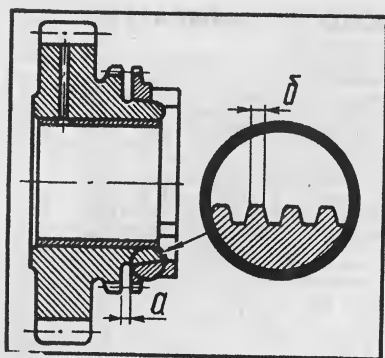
Установка синхронизирующих колец: а — зазор между торцом кольца и зубчатым венцом шестерни; б — площадка на вершине нитки резьбы.
